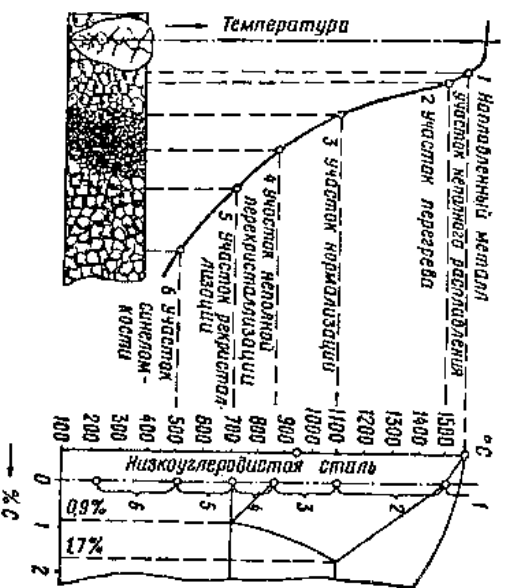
Строение зоны термического влияния сварного шва
